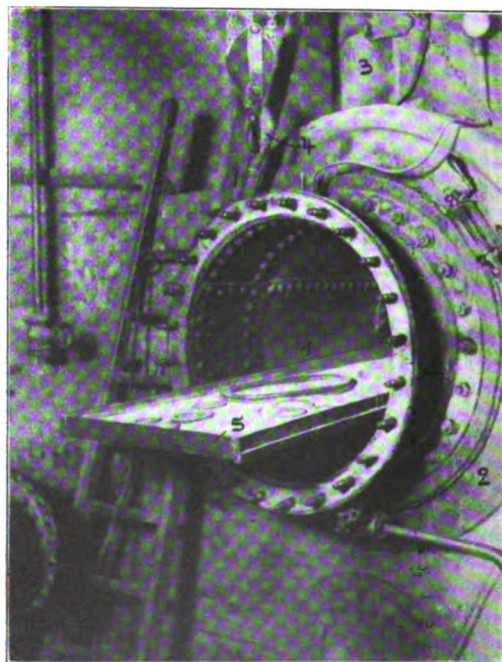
Vulkanisierkessel mit Dampfzeuger.
